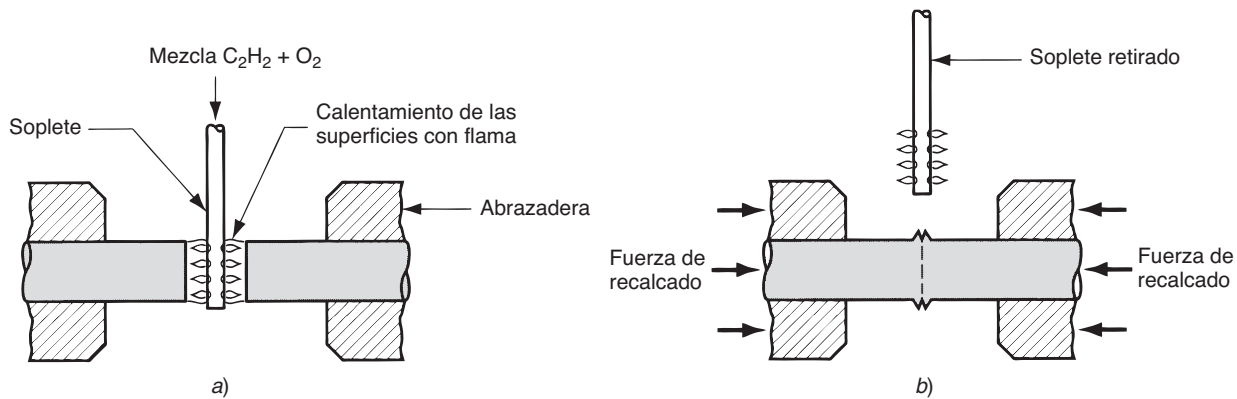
Una aplicación de soldadura con gas a presión: a) calentamiento de las dos piezas y b) aplicación de presión para formar la soldadura.
